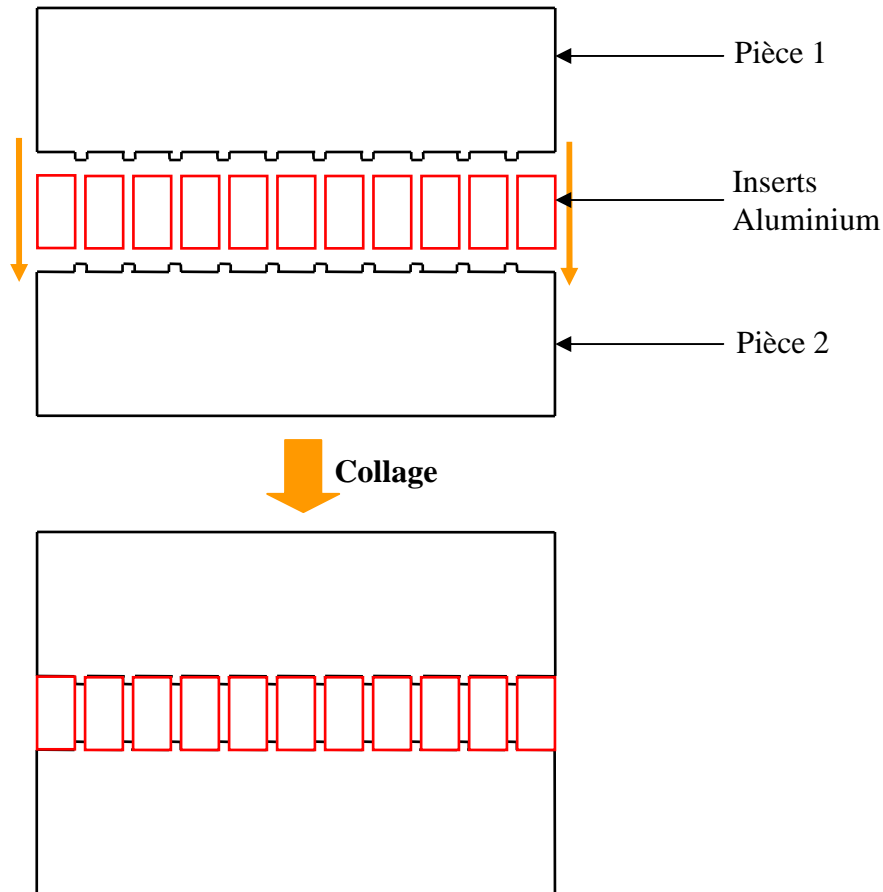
Schéma du collage de la section d'essais (vue du dessus).
